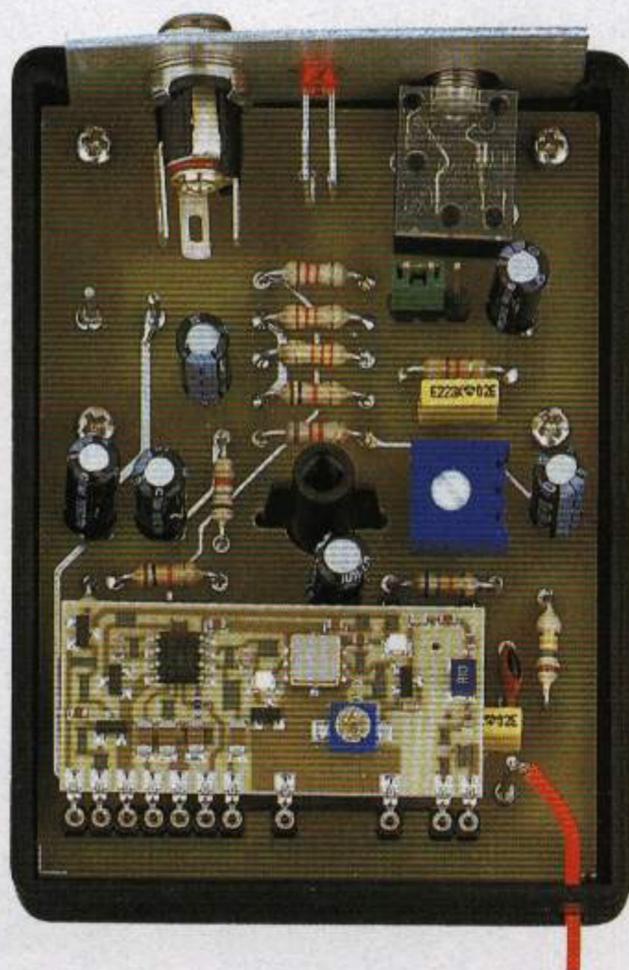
(Foto in alto) Prima di inserire il circuito stampato all'interno del mobile dove forare il pannello frontale per inserire la presa di alimentazione, far fuoriuscire la testa del diodo led e la presa femmina jack per il microfono.
